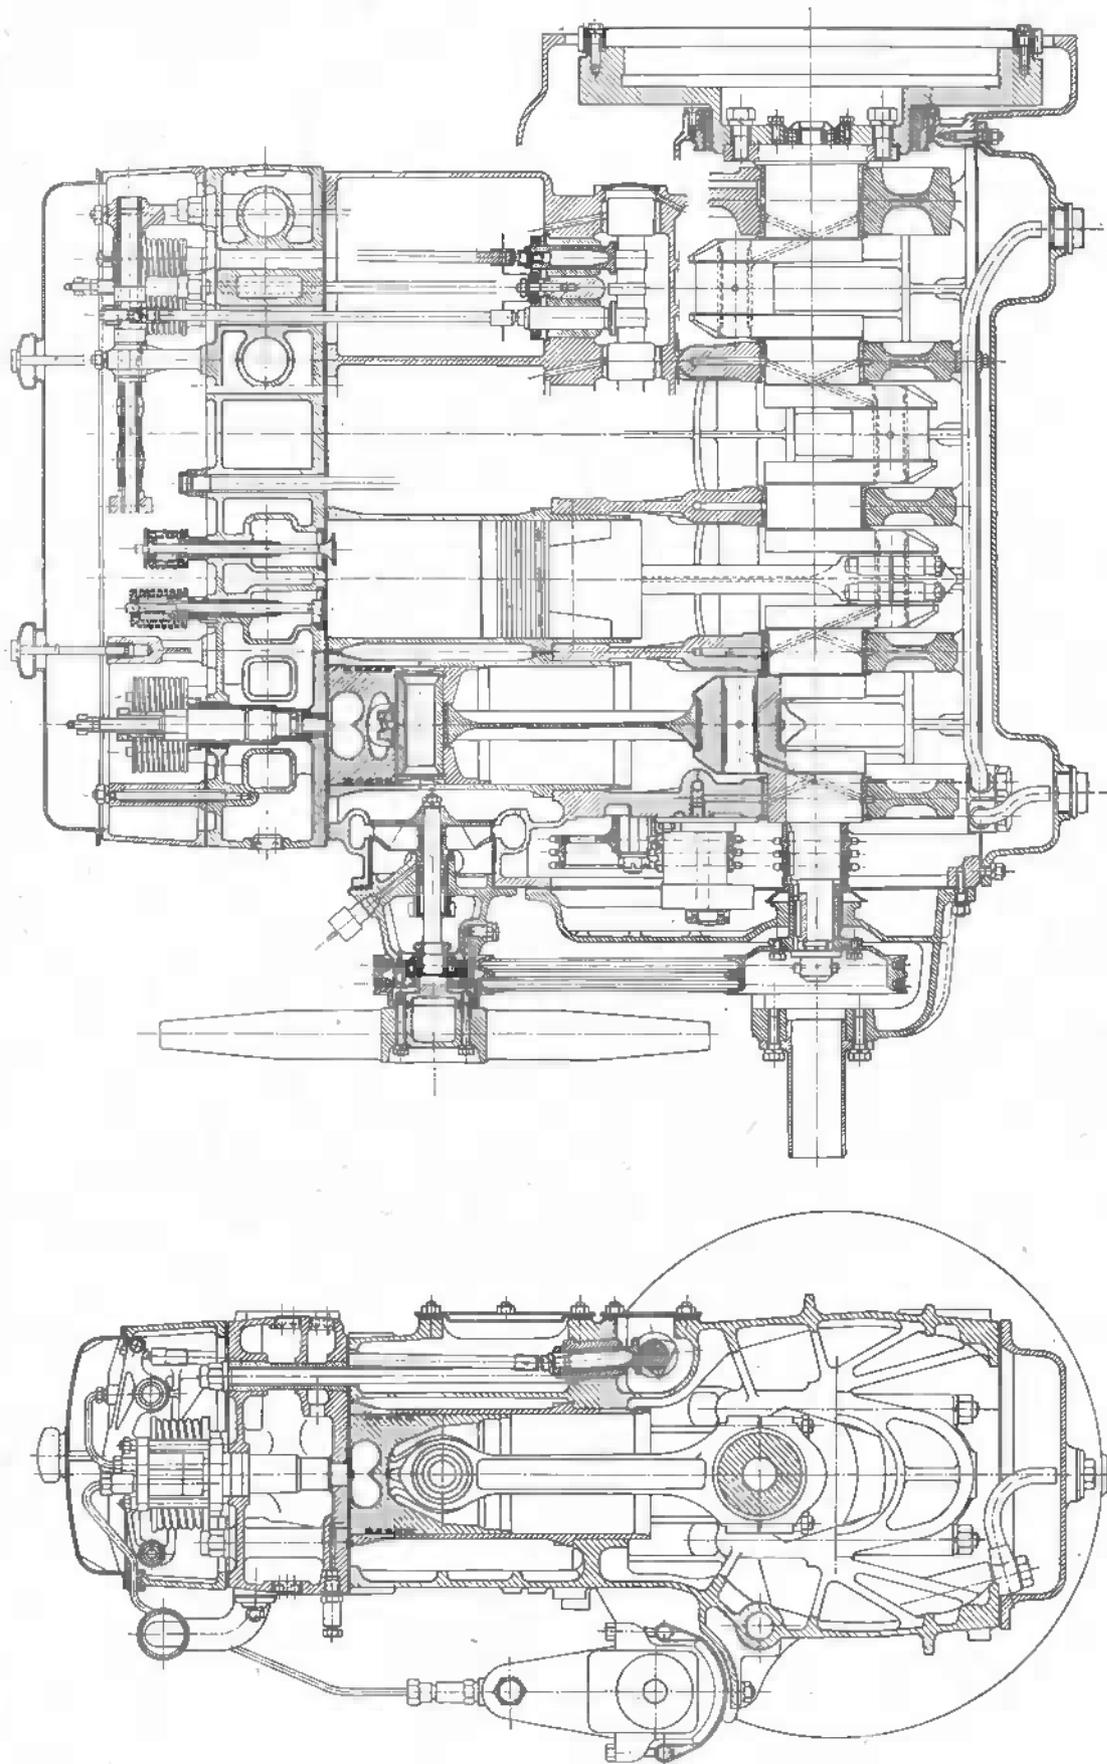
4-Zylinder-Fahrzeugmotor der Österreichischen Saurer Werke A. G.
